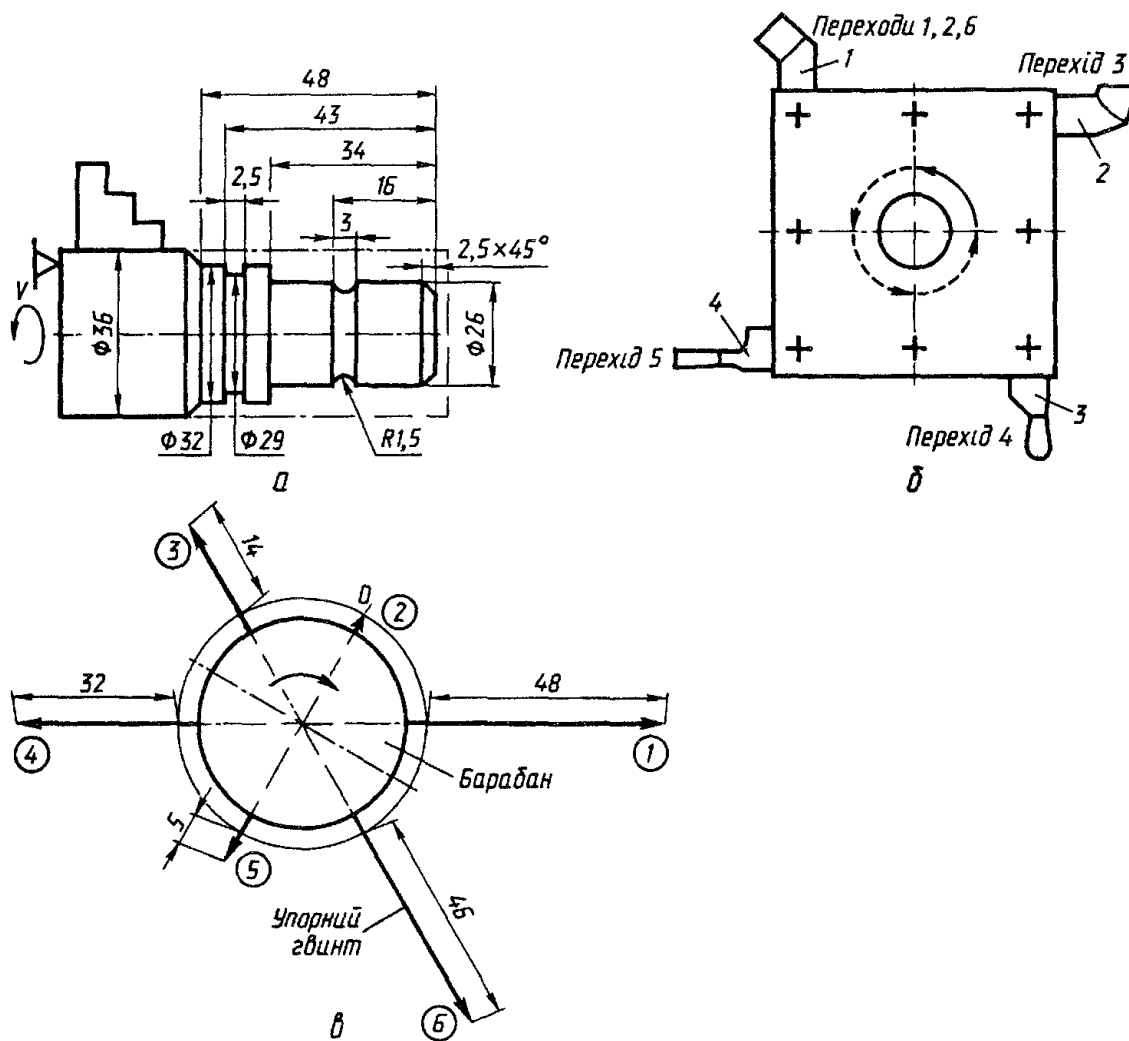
Наладка токарного верстата для оброблення ступінчастого вала за барабанним упором:
